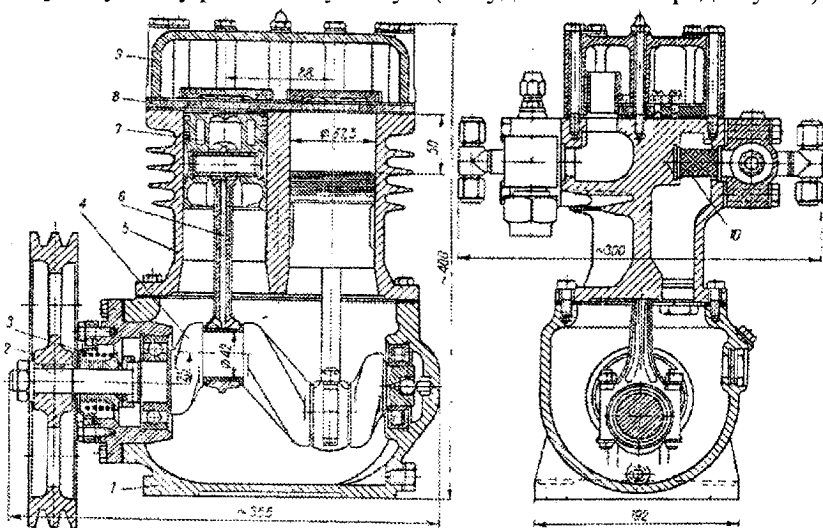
Фреоновий компресор ФВ-4: 1 – картер; 2 – маховик; 3 – сальфонний сальник; 4 – колінчастий вал; 5 – блок циліндрів; 6 – шатун; 7 – поршень; 8 – клапанна дошка; 9 – верхня кришка; 10 – сітчастий фільтр.
